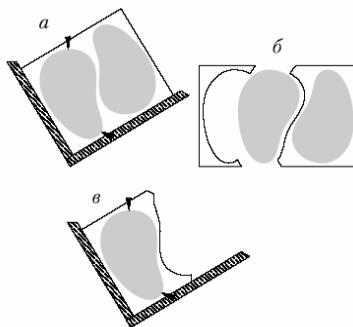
Этапы высечки из заготовок-двойников: *а* — закладка полосы в машину стопами; *б* — отделение верхней полосы от заготовки; *в* — поворот заготовки на 180° и закладка в машину для второго хода высечки
